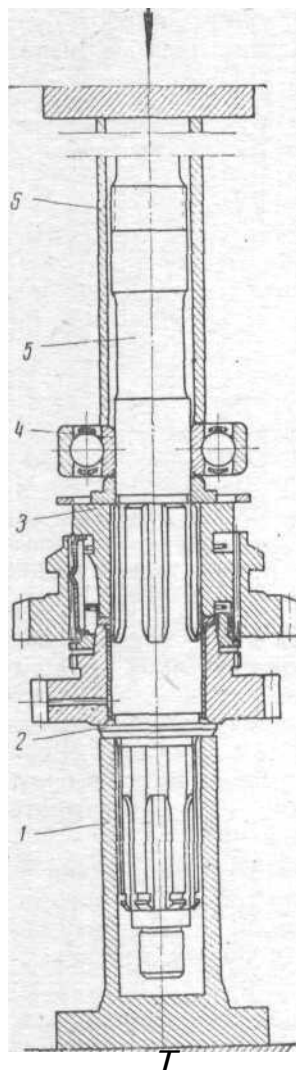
Напрессовка ступицы шестерни первой передачи и шарикового подшипника на ведомый вал
